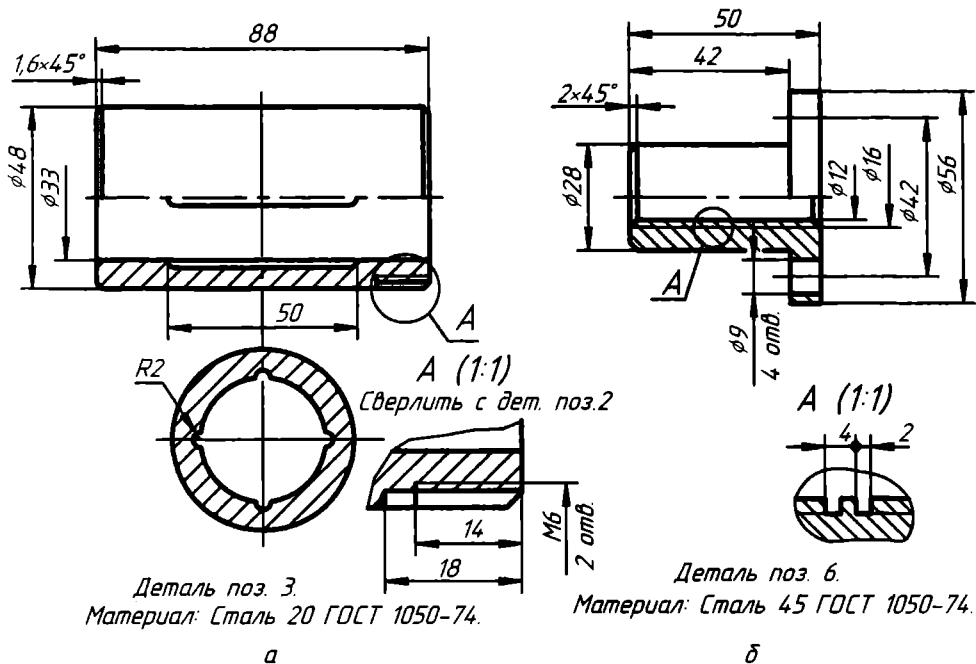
Чертежи: а — вкладыша; б — втулки
